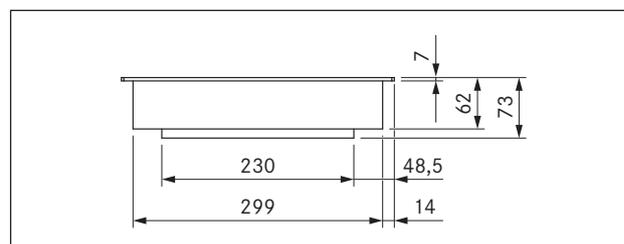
Dimensões do aparelho CKT, vista frontal
